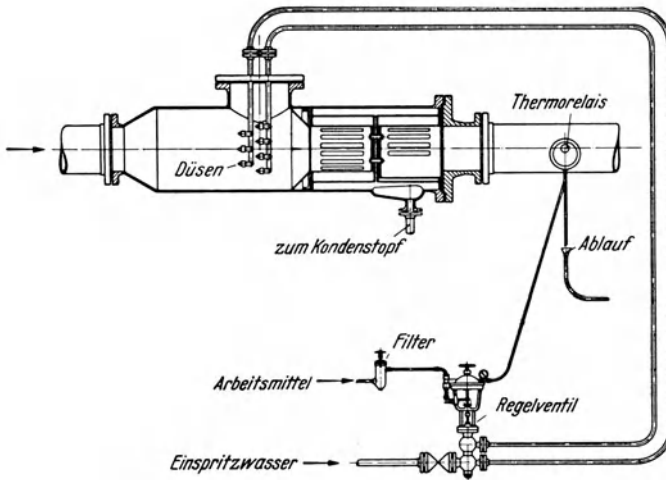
Heißdampfkühler mit Einspritzdüsen.
